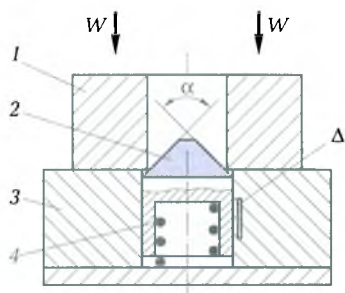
Схема установки детали с базовым отверстием на конический палец:
